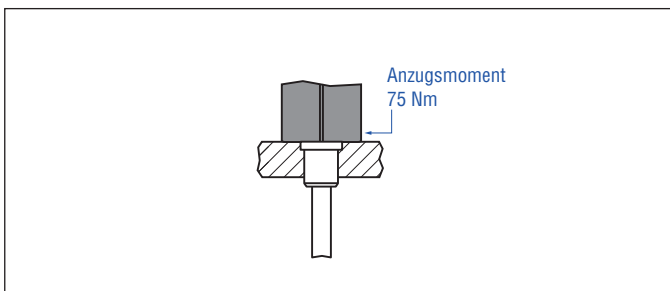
Einbaubeispiel für Gewindeflansch »F«, »M«, »S«, »W«
